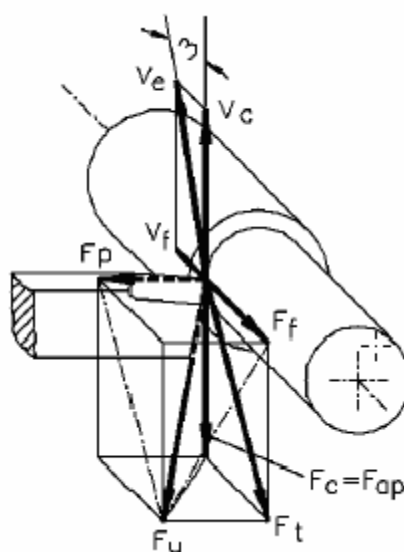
Componentes da Força de Usinagem no Torneamento. (13)
